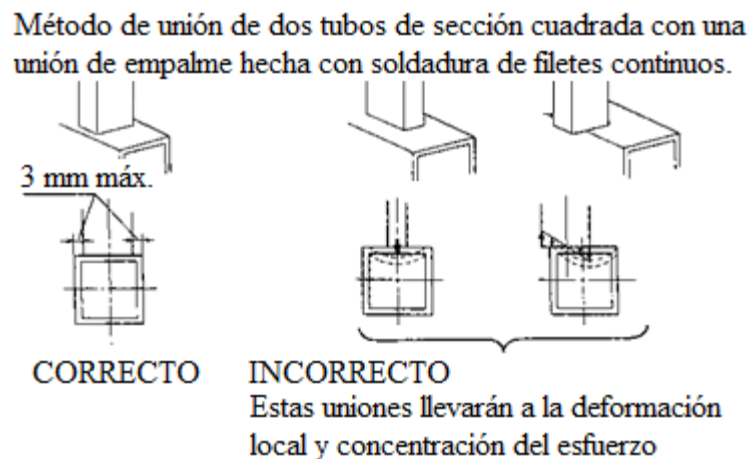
Unión de empalme hecha con soldaduras de filetes continuos
